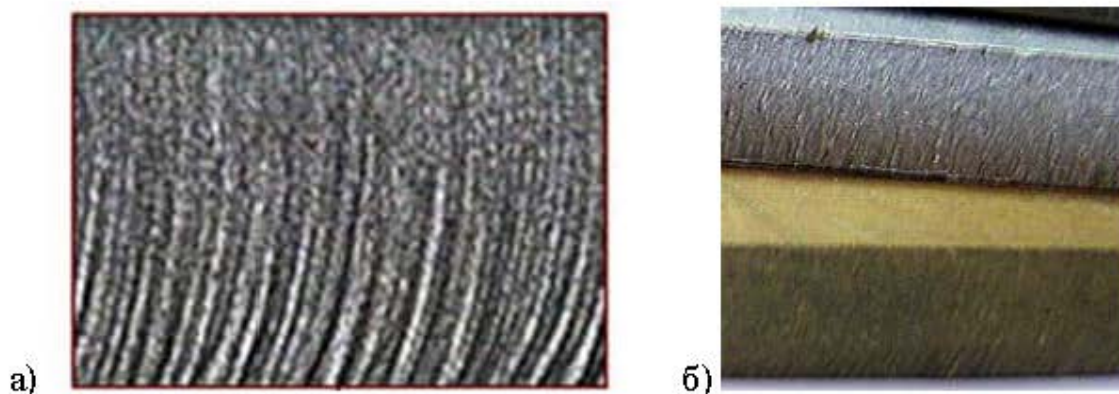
Дефекти поверхні обробки: а) запізнення струменя; б) задирки на зовнішній поверхні
